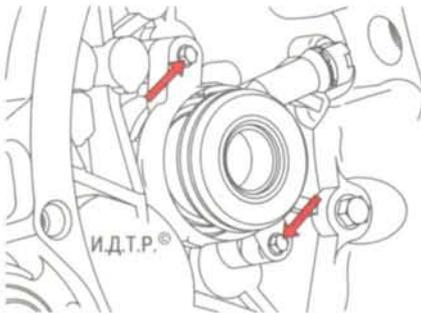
Расположение болтов крепления рабочего цилиндра гидропривода выключения сцепления
